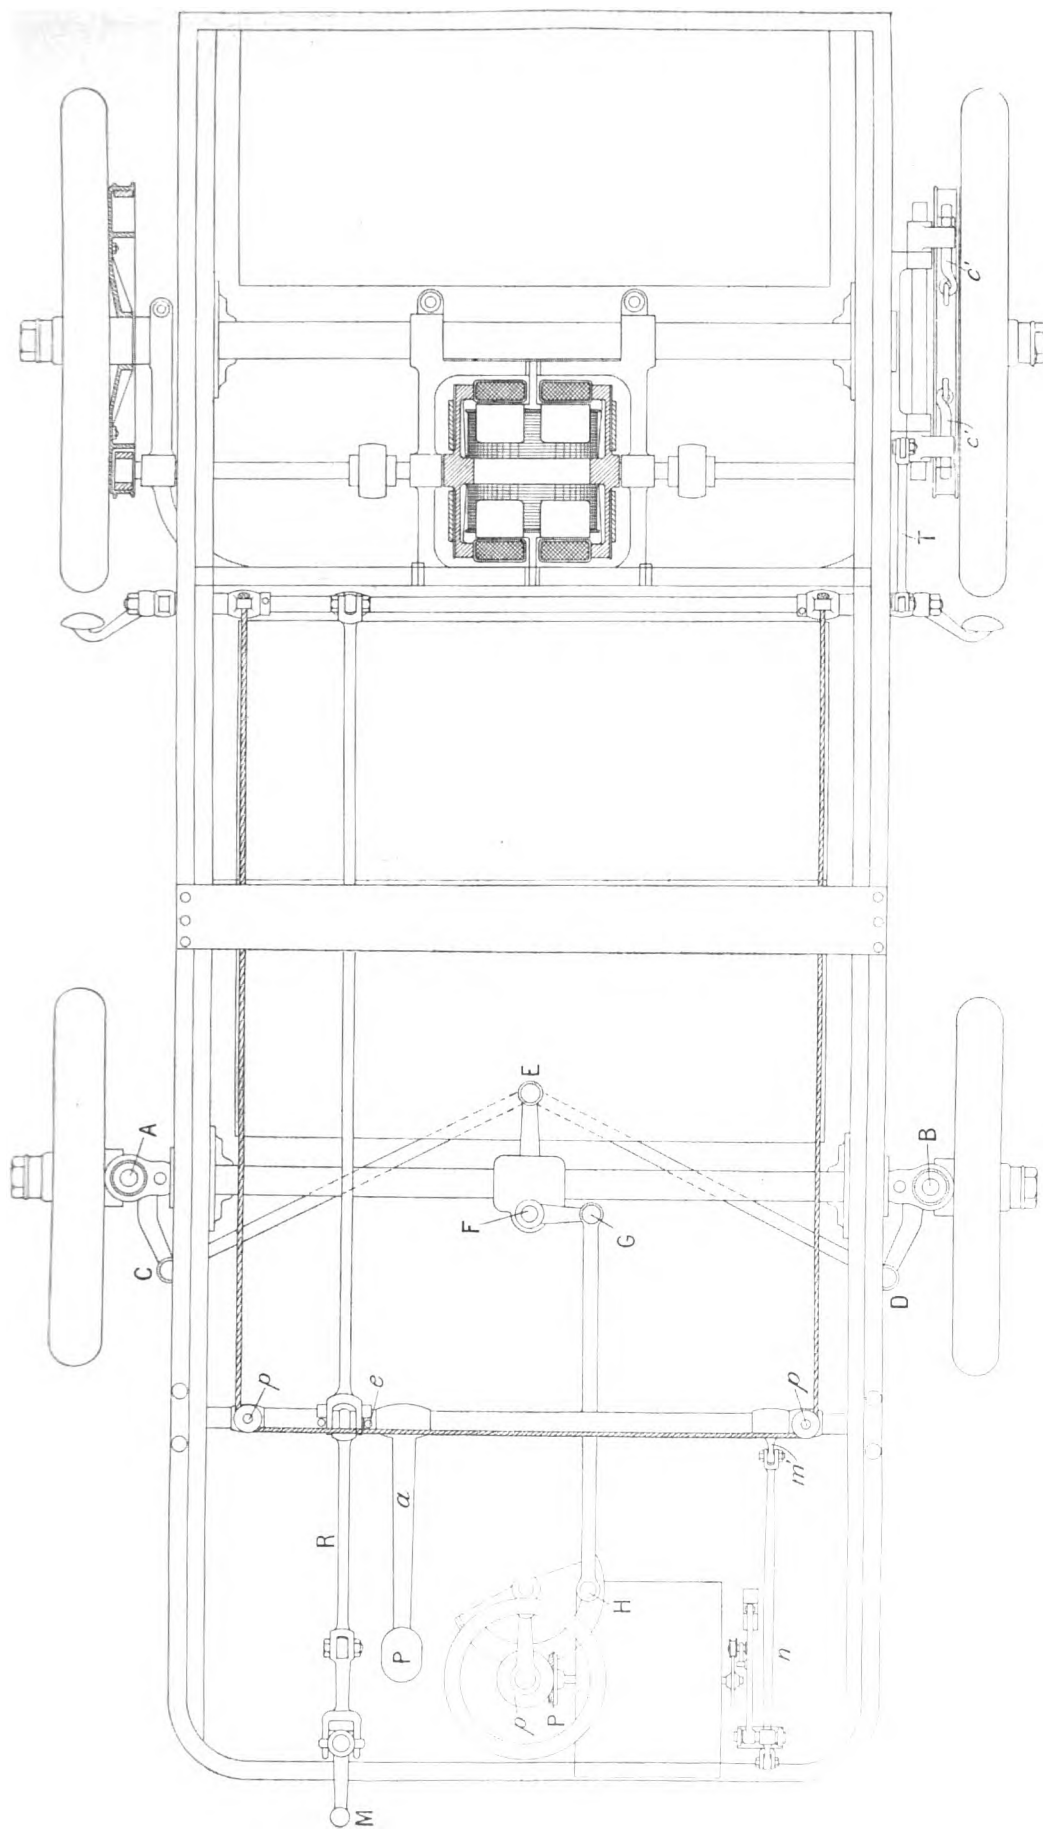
Plan d'ensemble de la voiture Meynier et Legros.
